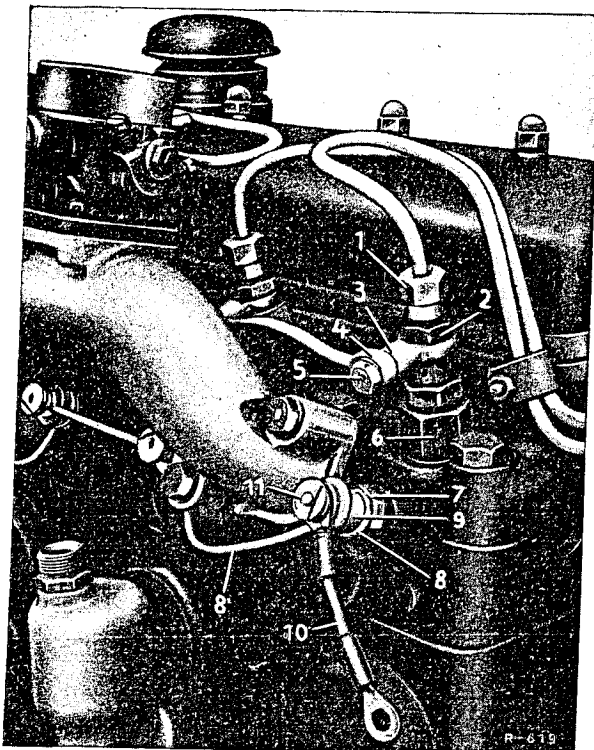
Zum Ausbau des Düsenhalters mit Einspritzdüse
